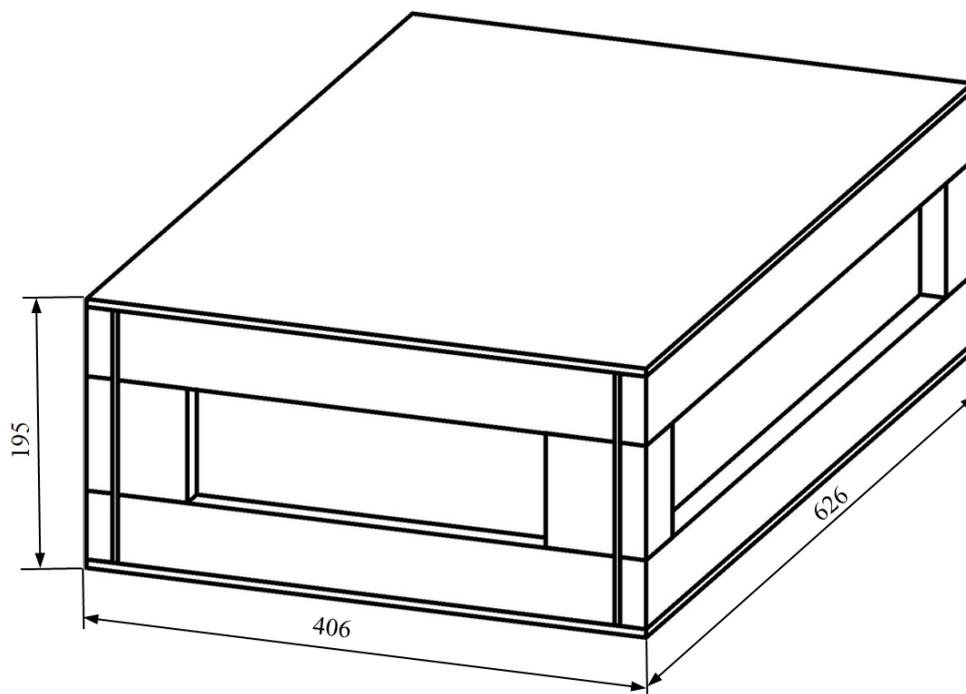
Габаритные размеры ящика транспортного ЯКУР.323361.033
